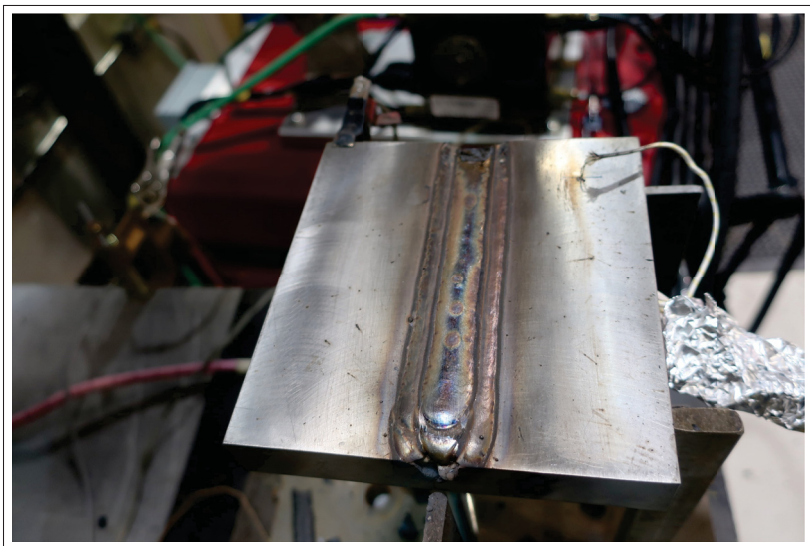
Plaque instrumentée après la complétion du soudage
